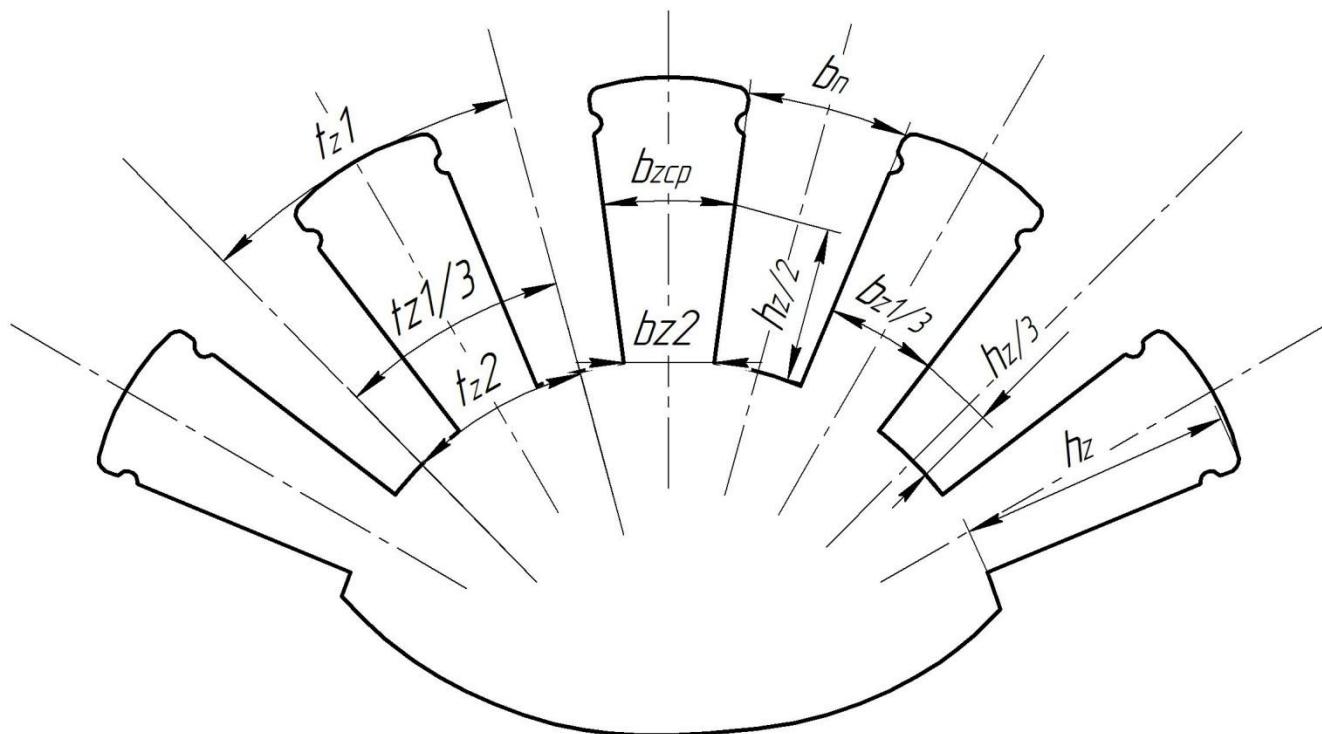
Зубчатый слой якоря и его размеры
